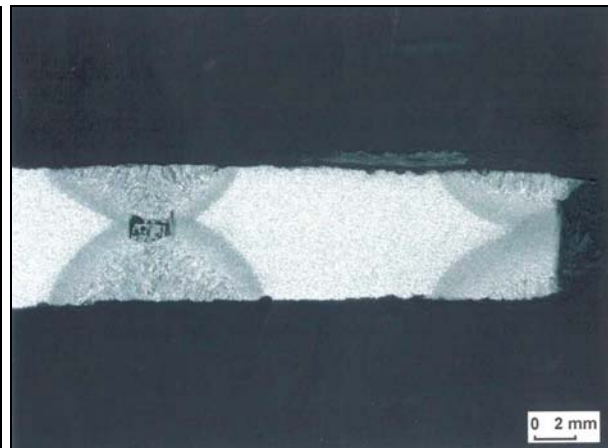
Makroschliff mit 2 Schweißnähten
